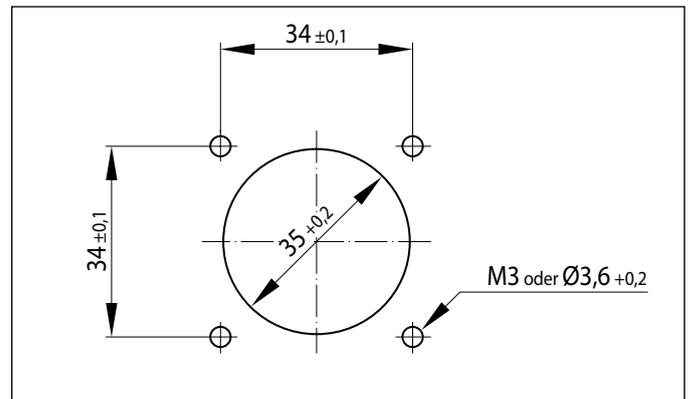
Maße und Anordnung der Montagebohrungen/Gewinde für Dose mit Flansch GA DF 1PL (Maße in mm)
